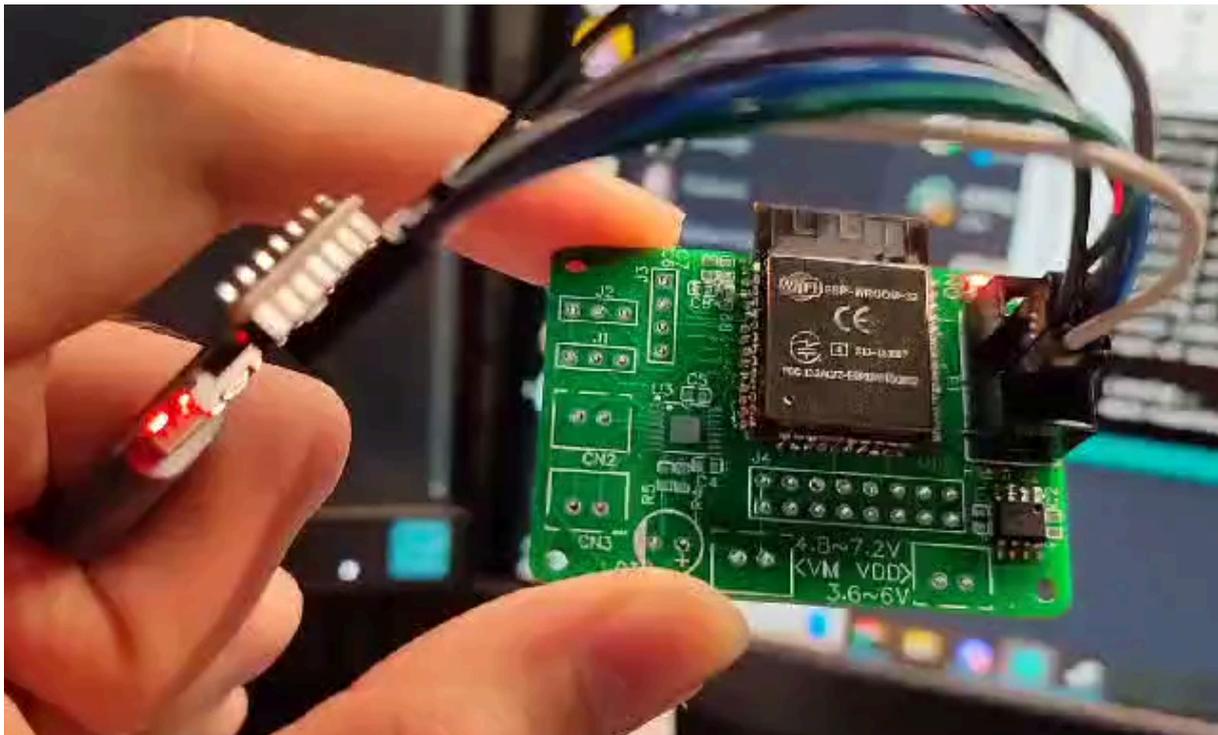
PCB del sistema con el conector de programación y ESP soldados.
